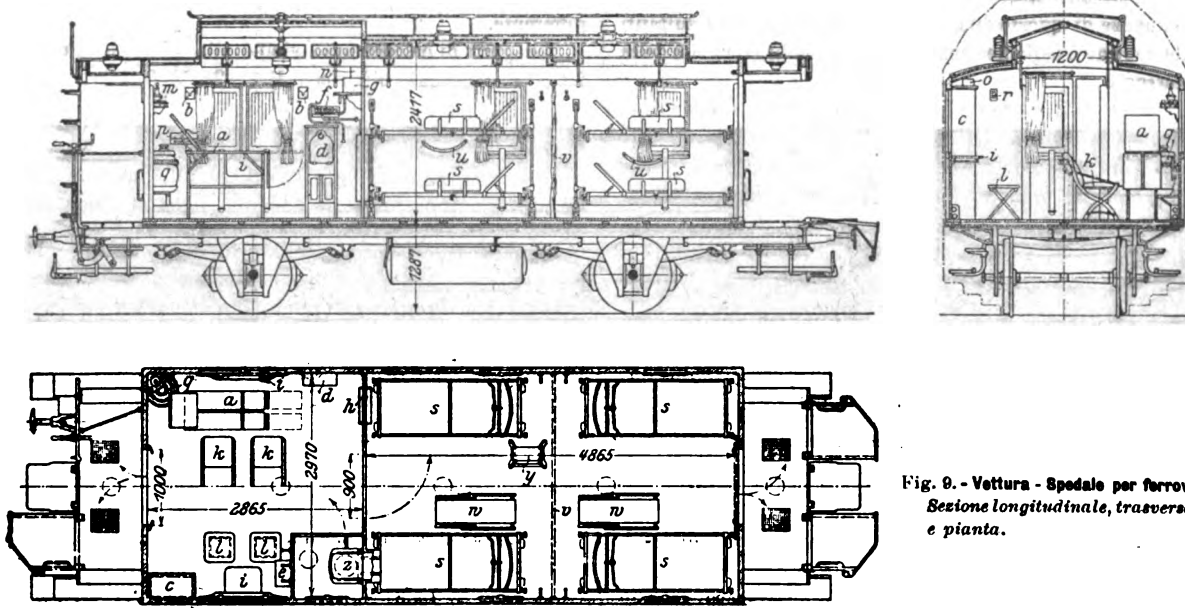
Vettura - Spedale per ferrovia. Sezione longitudinale, trasversale e pianta.
